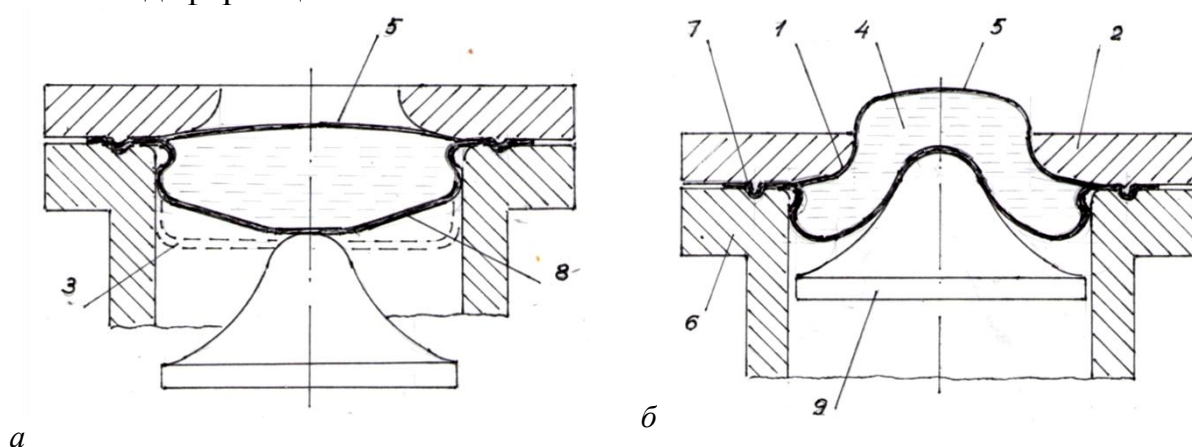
Схема расположения образца и инструмента в устройстве при испытании в исходном (а) и конечном положении (б): 1 – рабочее окно матрицы; 2 – матрица; 3 – мембрана; 4 – рабочая среда; 5 – образец; 6 – втулка; 7 – кольцеобразный зиг; 8 – усеченный конус мембраны; 9 – вкладыш
